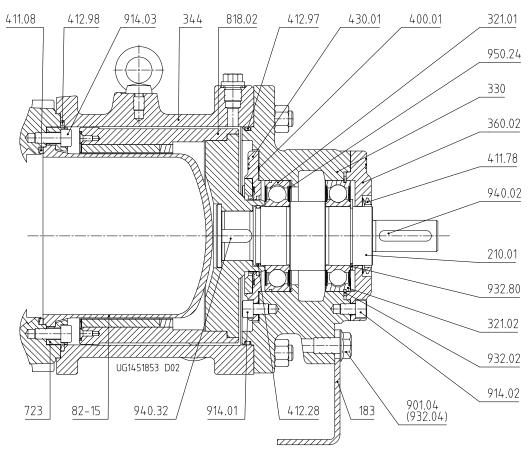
Ausführung Lagerträger mit Fettschmierung und Wellendichtring als Leckagebarriere
